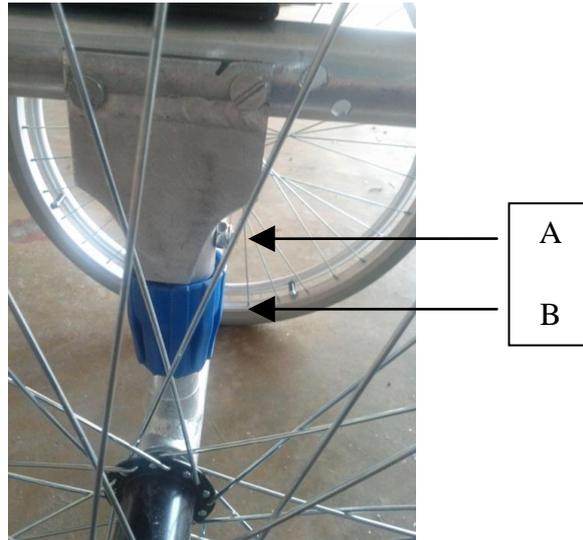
Sistema de elevação e de alteração do centro de gravidade da cadeira
